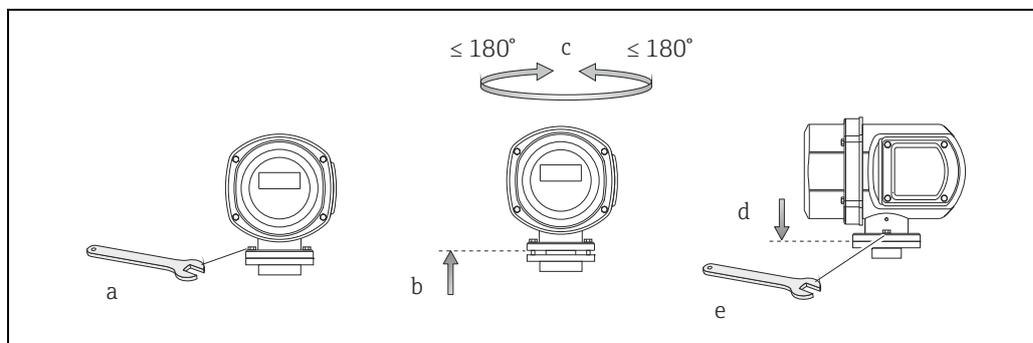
Поворот полевого корпуса преобразователя из нержавеющей стали
